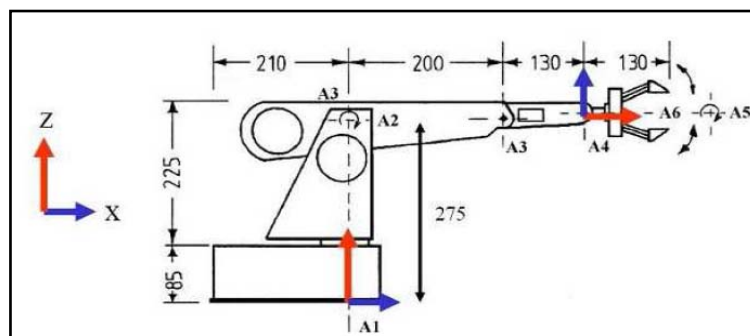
Les dimensions du robot ROB3 (vue de face).
